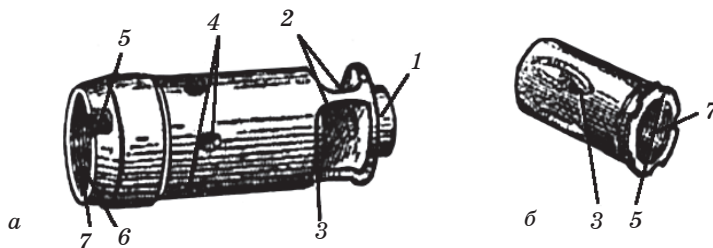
Дульный тормоз-компенсатор и пламегаситель: *a* — дульный тормоз-компенсатор; *б* — пламегаситель. 1 — венчик; 2 — окна; 3 — цель; 4 — компенсационные отверстия; 5 — выем для фиксатора; 6 — скос; 7 — внутренняя резьба
